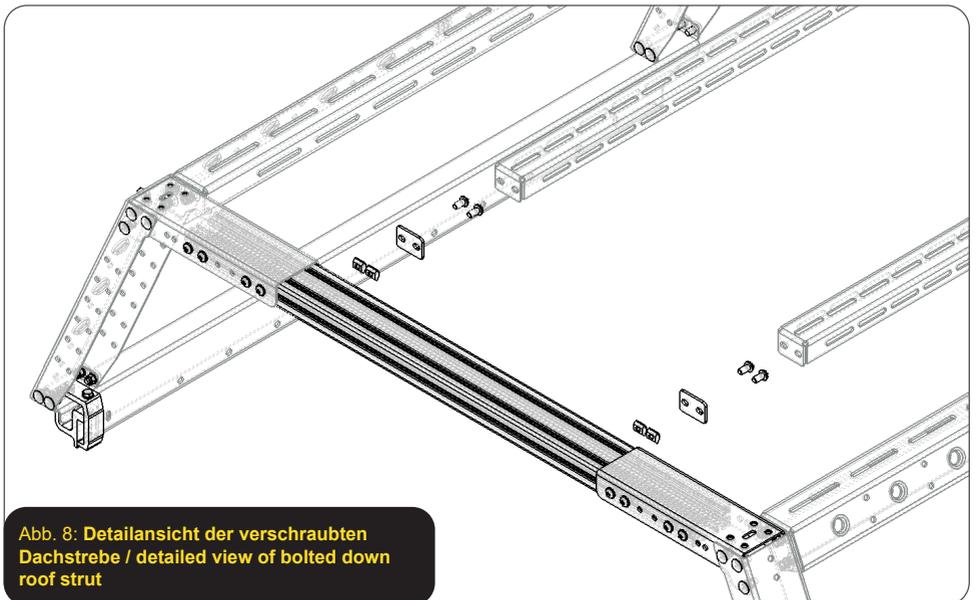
Detailansicht der verschraubten Dachstrebe / detailed view of bolted down roof strut
